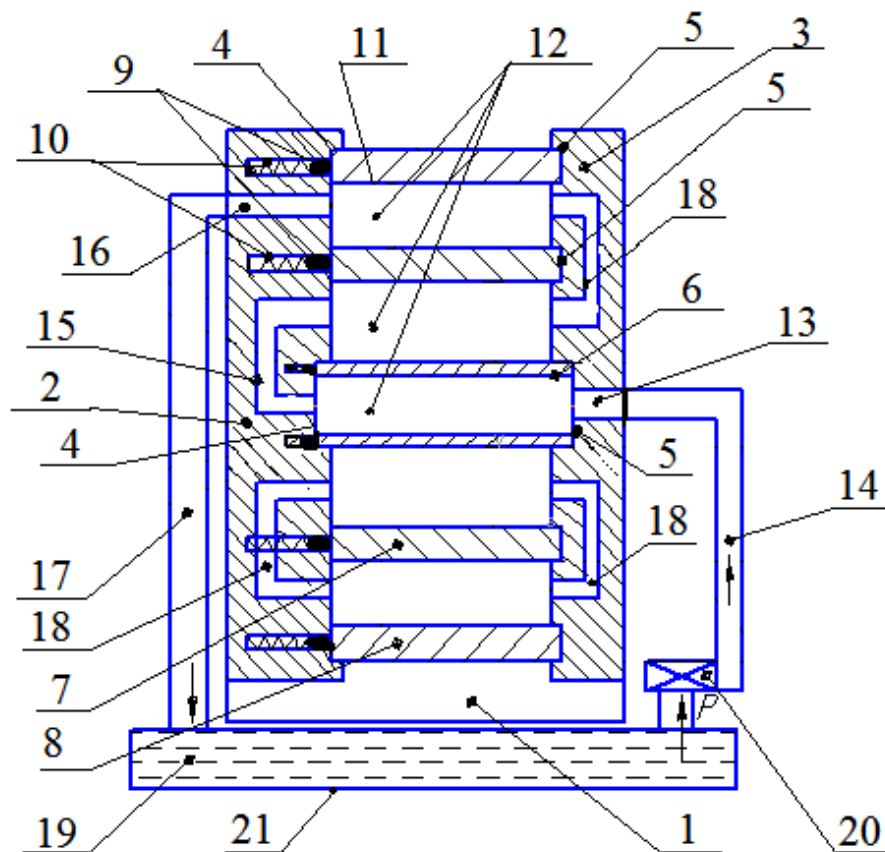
Устройство для гидроабразивной обработки внутренних и наружных поверхностей трубных заготовок
